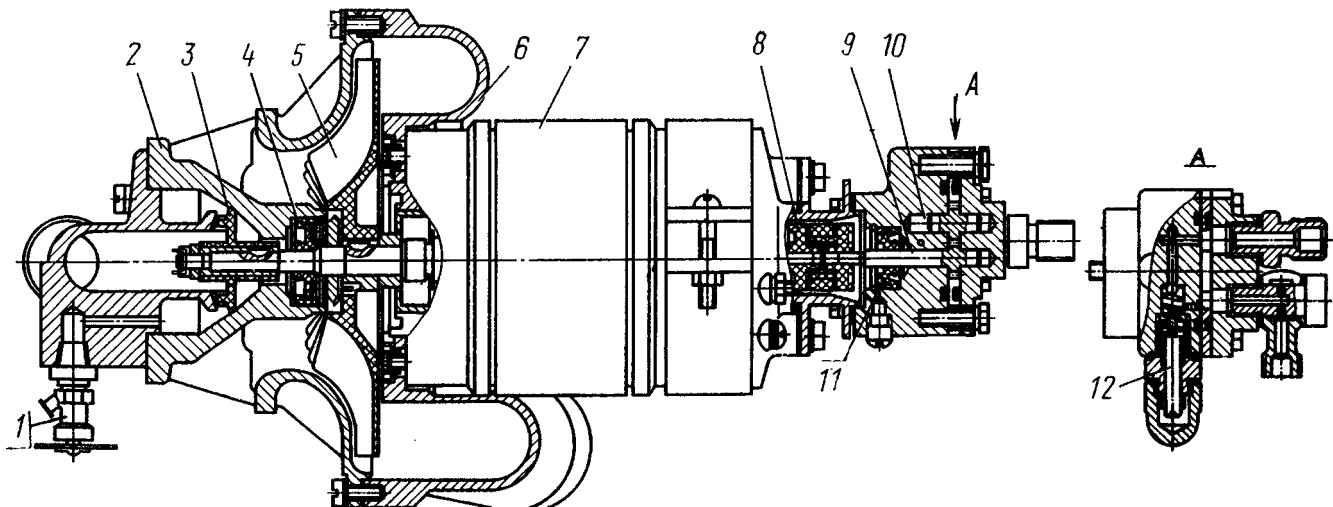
Насосный агрегат: 1 - кранник сливной; 2 - корпус жидкостного насоса; 3 - колесо рабочее жидкостного насоса; 4, 11 - манжеты уплотнительные; 5 - крыльчатка вентилятора; 6 - корпус вентилятора; 7 - электродвигатель; 8 - муфта топливного насоса; 9 - шестерня ведущая топливного насоса; 10 - шестерня ведомая топливного насоса; 11 - клапан редукционный
